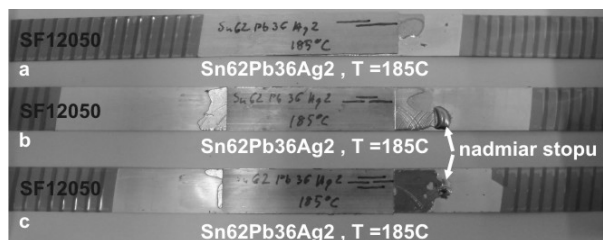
Przygotowanie taśmy HTS 2G do połączenia
